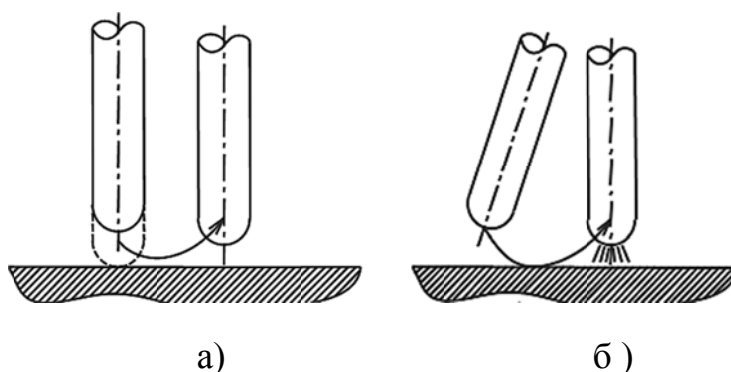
Приемы возбуждения дуги при сварке:
